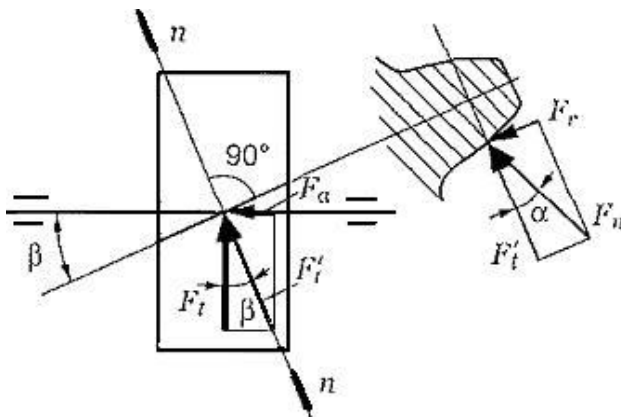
Схема действия сил в зацеплении косозубых колес
